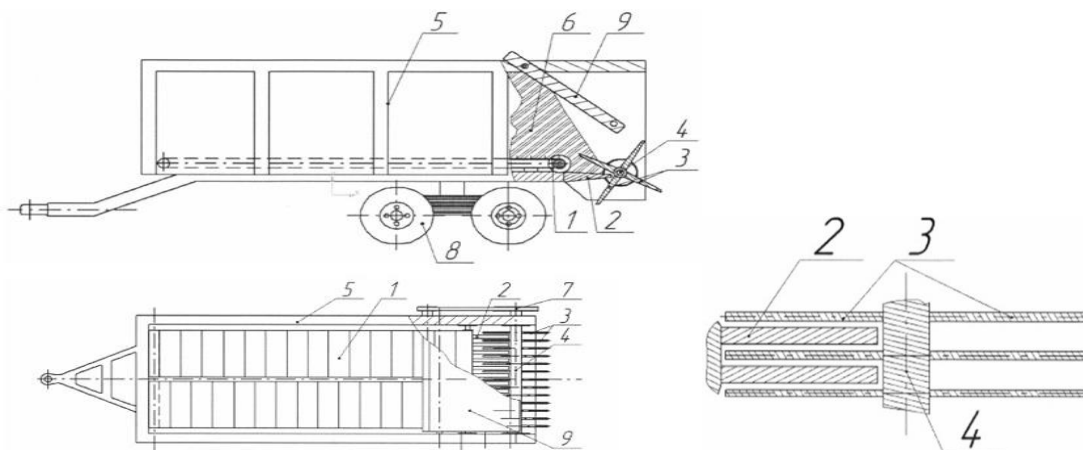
Разбрасыватель-измельчитель подстилочного навоза (1 - цепочно-планчатый транспортер; 2 – противорежущие пластины; 3 – ножи; 4 – вал; 5 – кузов; 6 – овечий навоз; 7 – привод ножевого вала; 8 – колеса; 9 – борт)
